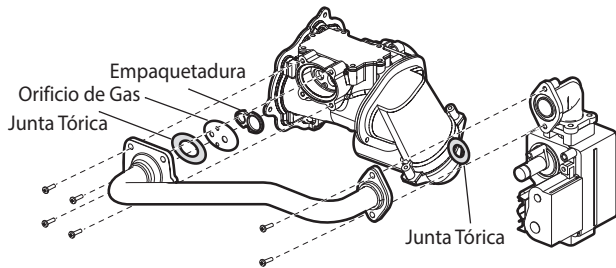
Vista Detallada del Conjunto de Tubo de Gas
